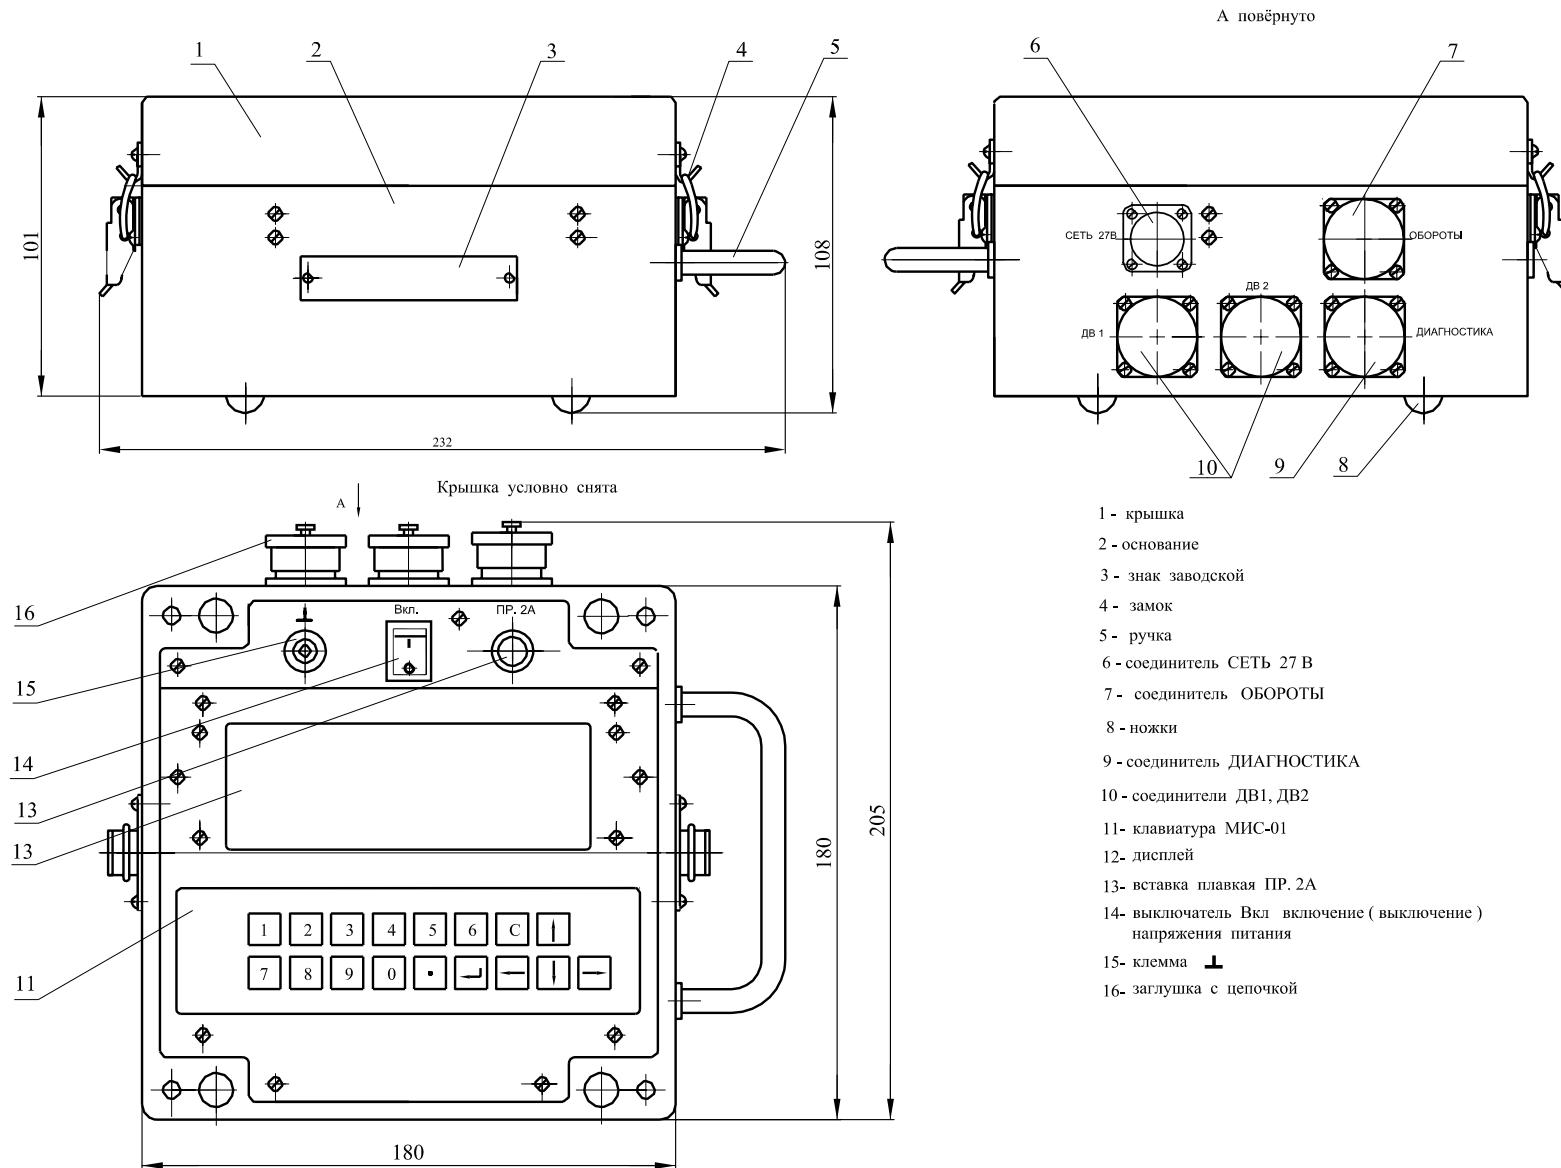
Габаритно-установочные размеры блока электронного БЭ-40-4М-2.1
